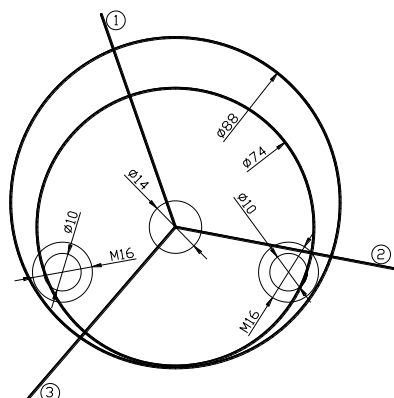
Эксцентричное расположение ротора в корпусе
